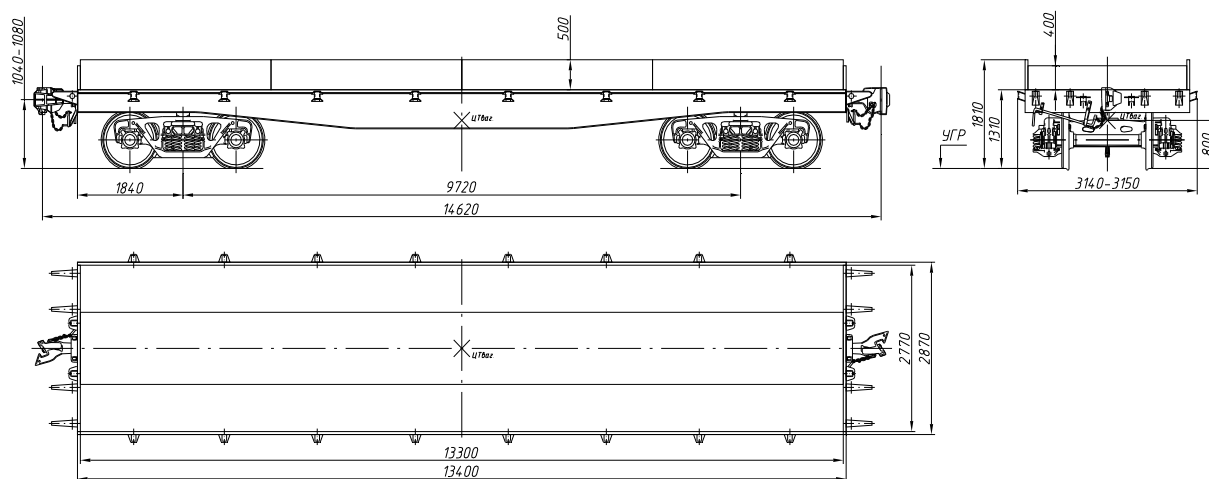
Общий вид 4-осной универсальной железнодорожной платформы
